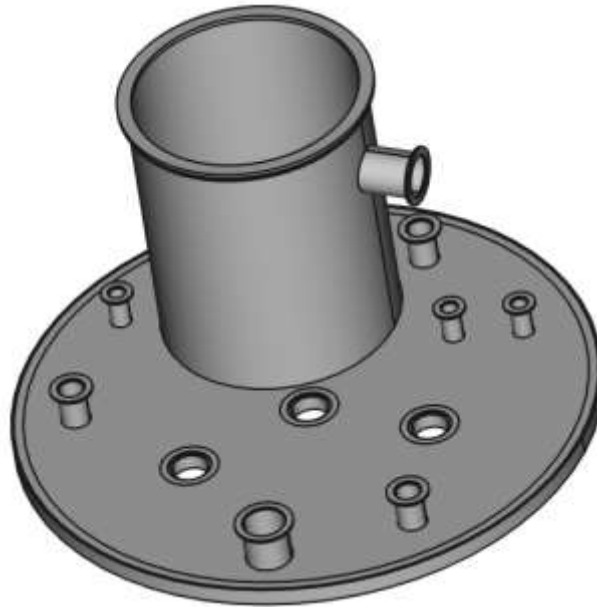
Flangia inferiore. La vista della flangia inferiore è rovesciata per far vedere tutti gli attacchi presenti nella parte inferiore della camera
